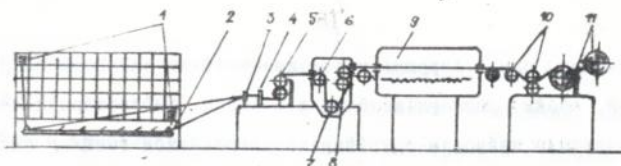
Схема установки для виготовлення безперервної склопластикової стрічки: 1 - бобіни зі склониткою; 2 - збірна планка; 3 - ниткозбірне кільце; 4 - розподільний прилад або розсікач потоку ниток; 5 - натяжна виделка; 6 - направляючий валик; 7 - просочувальний валик; 8 - віджимний прилад; 9 - сушильна камера; 10 - валики приймального пристрою; 11 - приймальні касети намотуючого пристрою.
